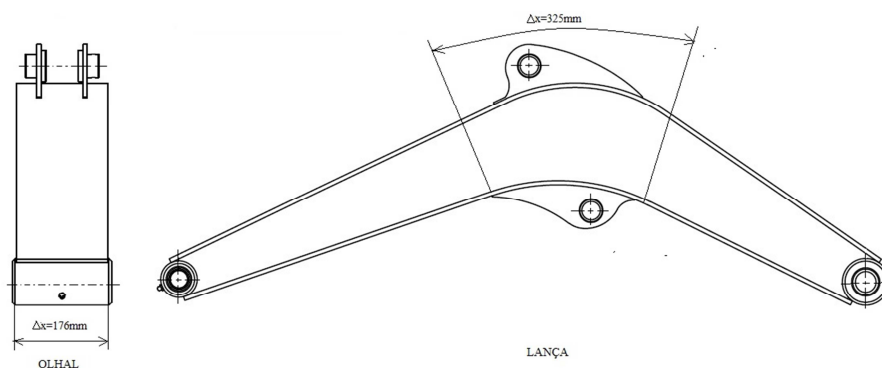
Representação dos cordões de soldadura considerados
